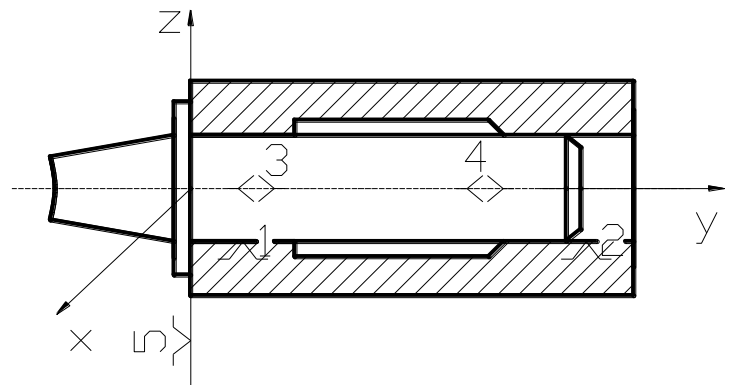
Базування по довгій внутрішній поверхні обертання (з зазором)
